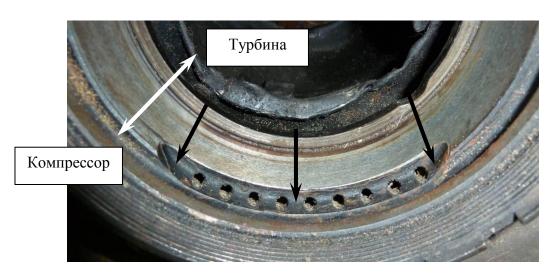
Проточка, предназначенная для слива масла, в корпусе камеры сгорания (расположена со стороны компрессора).
